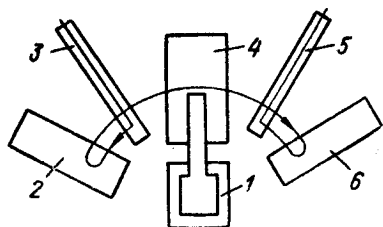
Схема розташування робота для обслуговування трьох верстатів:
